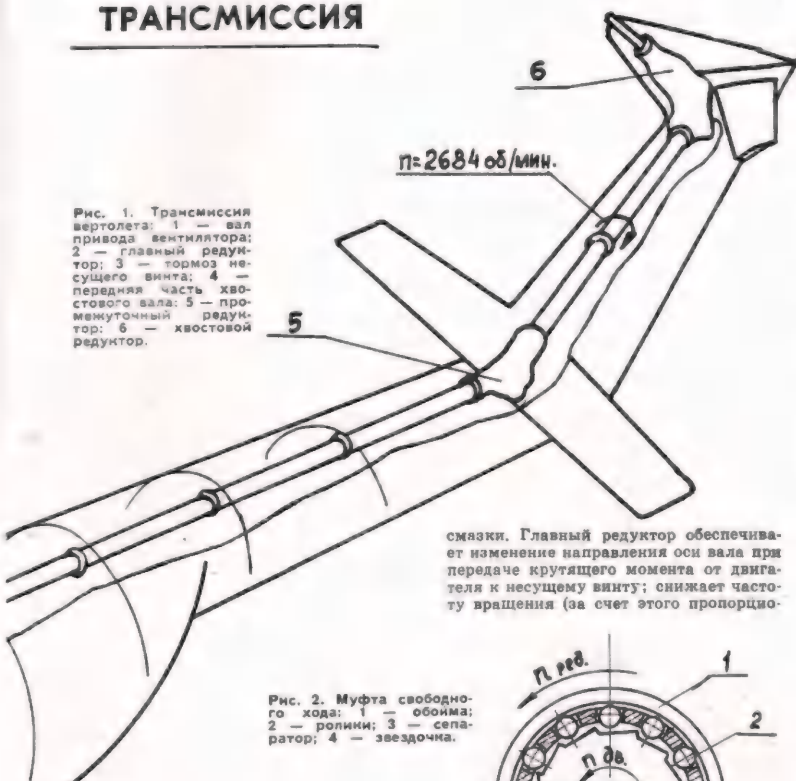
Трансмиссия вертолета: 1 — вал привода вентилятора; 2 — главный редуктор; 3 — тормоз несущего винта; 4 — передняя часть хвостового вала; 5 — промежуточный редуктор; 6 — хвостовой редуктор.
